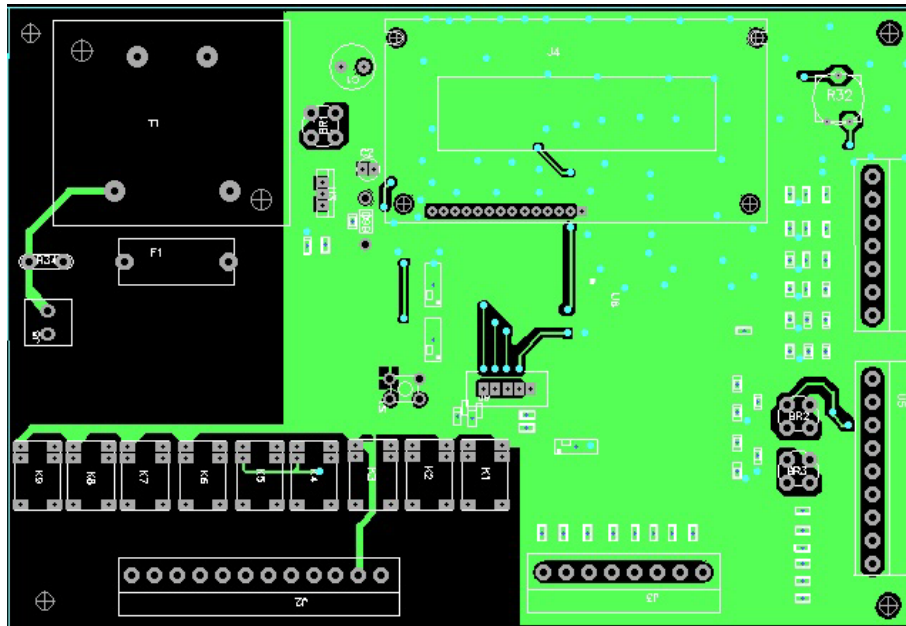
Impressió pantalla cara inferior PCB (BOTTOM)
